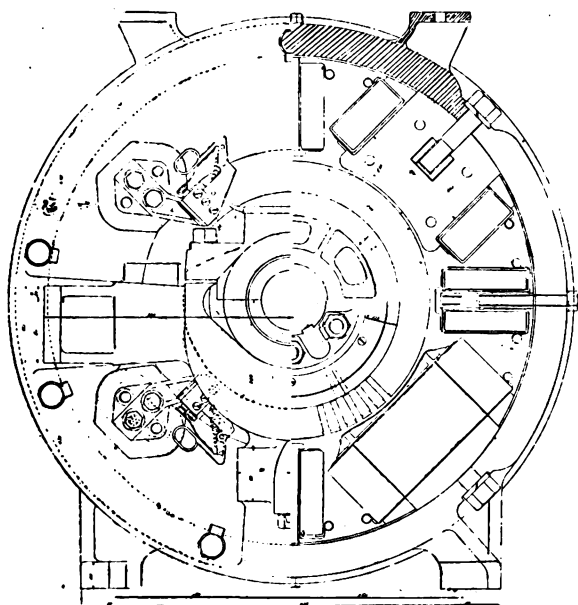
ter. — Coupe et élévation transversale du moteur.
